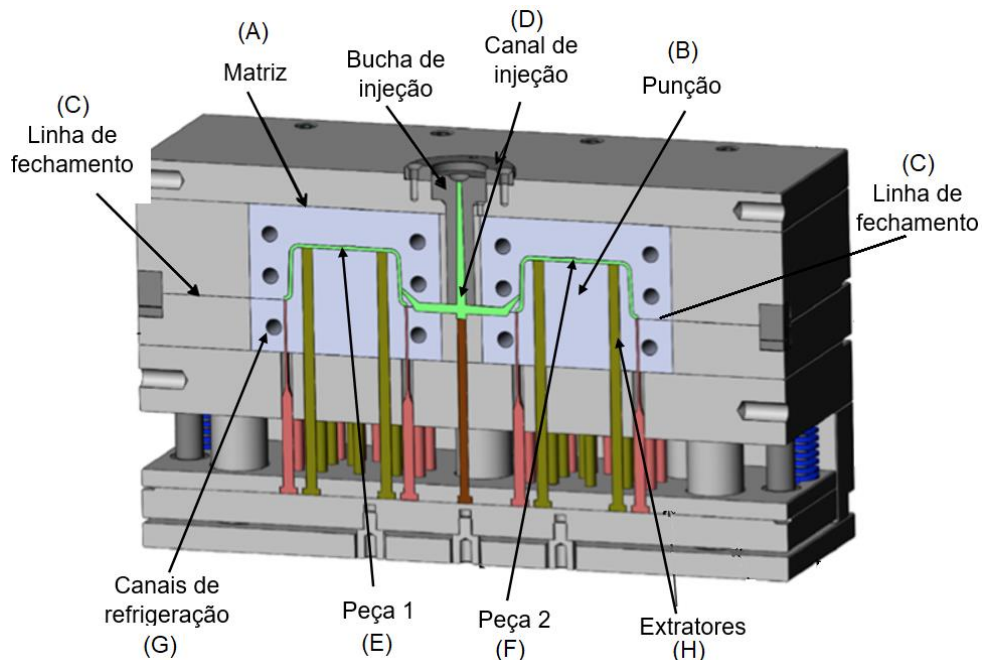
Principais componentes de um molde de injeção de duas cavidades.
